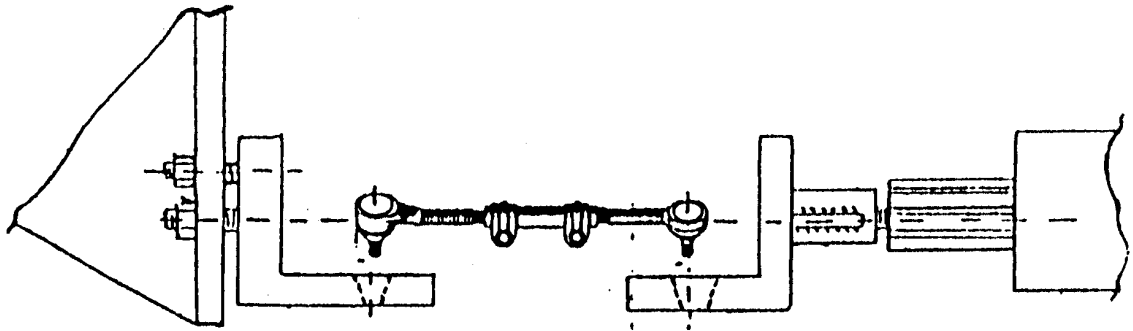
Dispositivo de fijación para el ensayo de fatiga.
